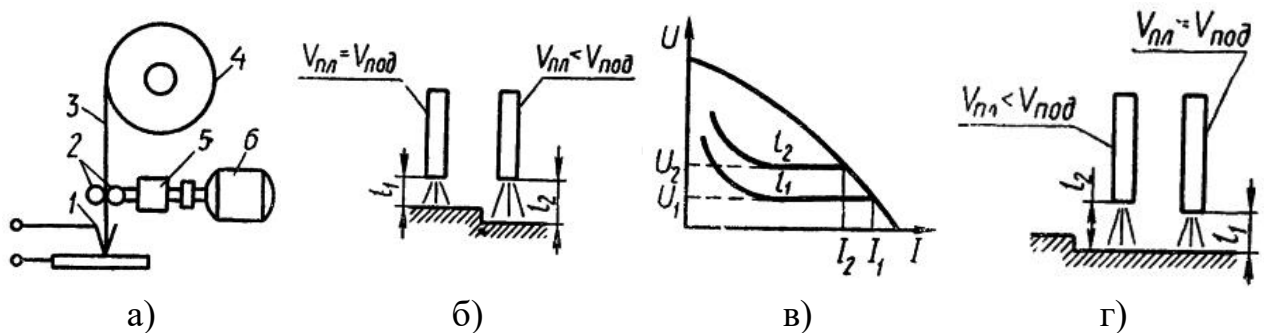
Схеми пристрою зварювального автомату та пресу саморегулювання довжини дуги
